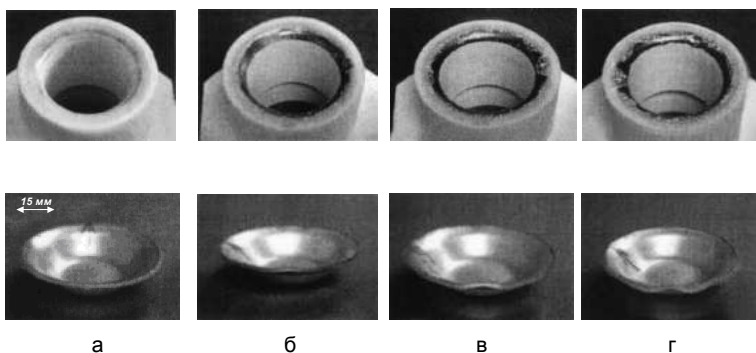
Износ матриц после вытяжки: а - 1006 заготовок; б - 1035 заготовок; в - 1509 заготовок; г - 1787 заготовок
